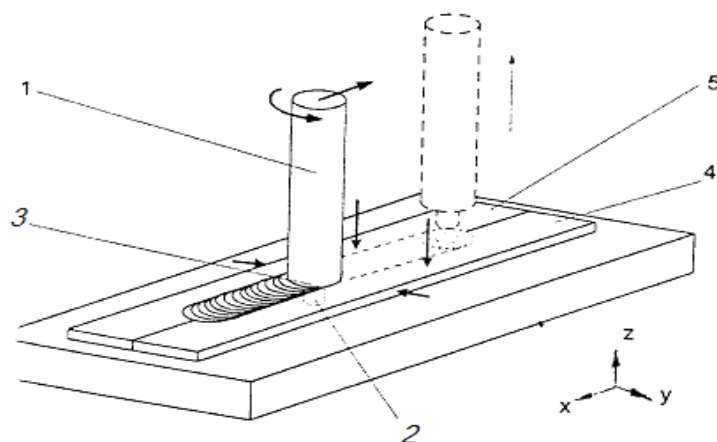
Схема процесса СТП: 1 – корпус инструмента;
